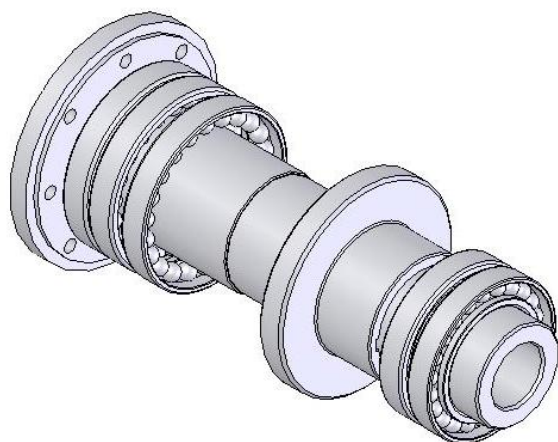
3D конструкція шпиндельного вузла верстата
